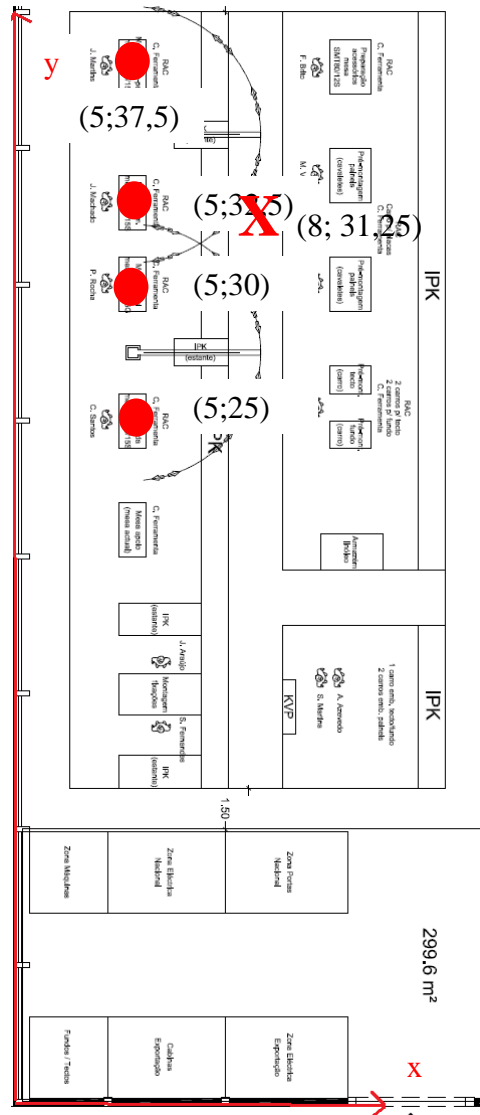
Layout Schmitt Elevadores, secção de Montagem (P04).
